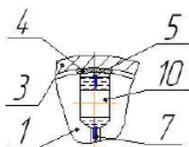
Вариант исполнения устройства для автобалансировки заготовок с балансировочными цилиндрами
